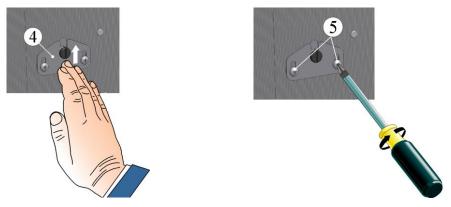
Appuyer sur les plaques de fixation et les bloquer (figure similaire)
